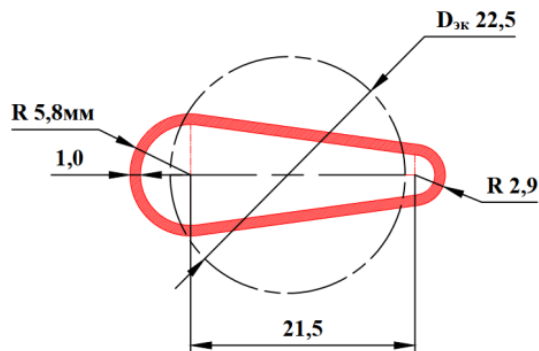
Поперечное сечение каплевидной трубы без нагрузки
